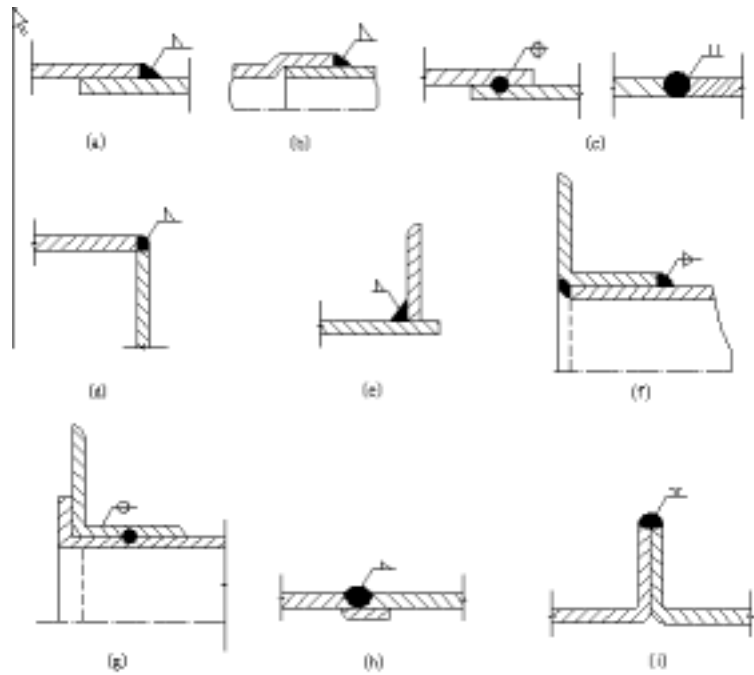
6. 1. 2-14 属风管焊接接头形式
